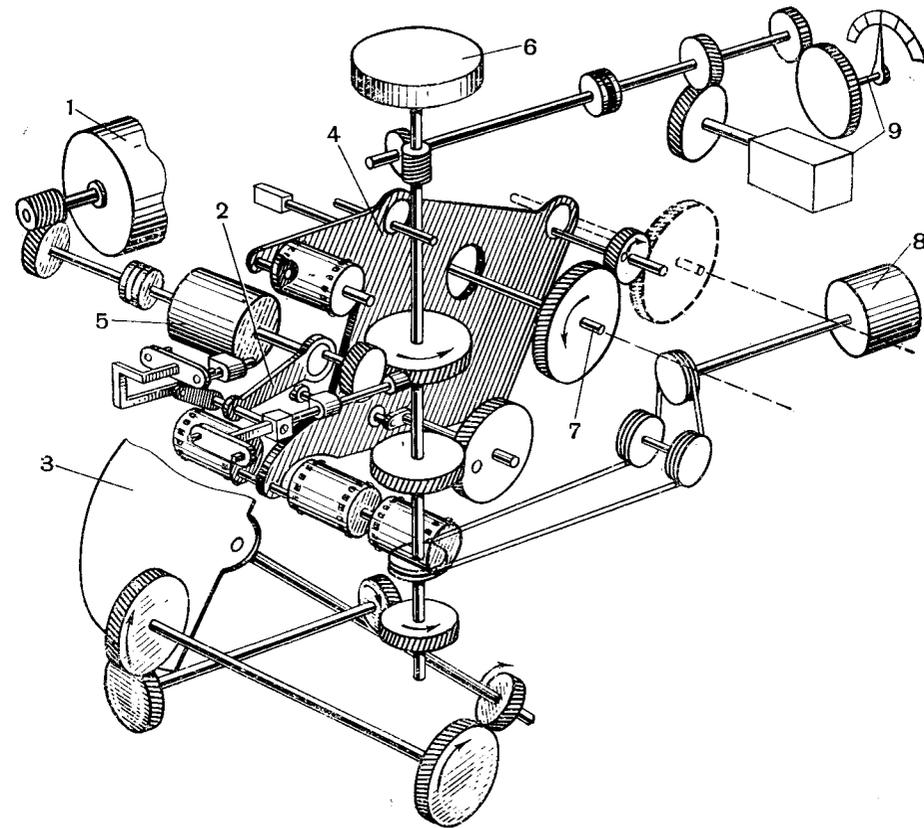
Кинематическая схема аппарата «Родина»: 1 — электродвигатель, 2 — грейферный механизм, 3 — зеркальный обтуратор, 4 — кулиса, 5 — маховик на оси грейферного механизма, 6 — маховик на вертикальном валу, 7 — ось фрикциона кассеты, 8 — тахометр, 9 — счетчики
